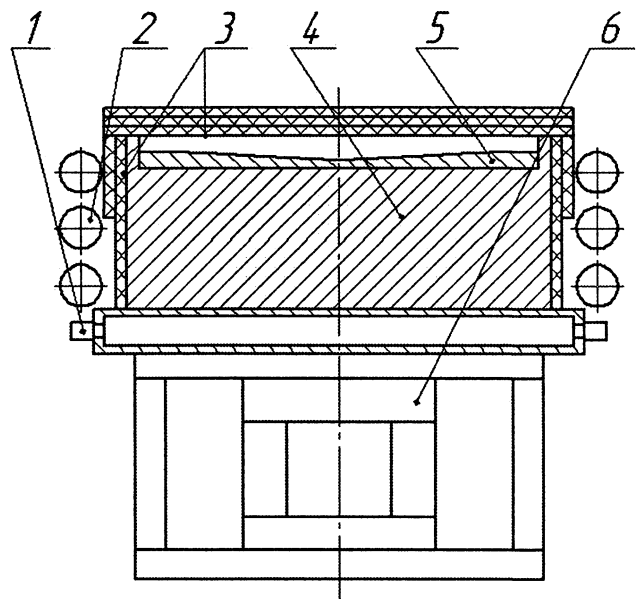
Схема получения плоских биметаллических заготовок: 1 — подставка; 2 — индуктор; 3 — теплоизоляционный материал; 4 — стальная основа; 5 — наплавленный слой; 6 — пневматическое вибрационное устройство
